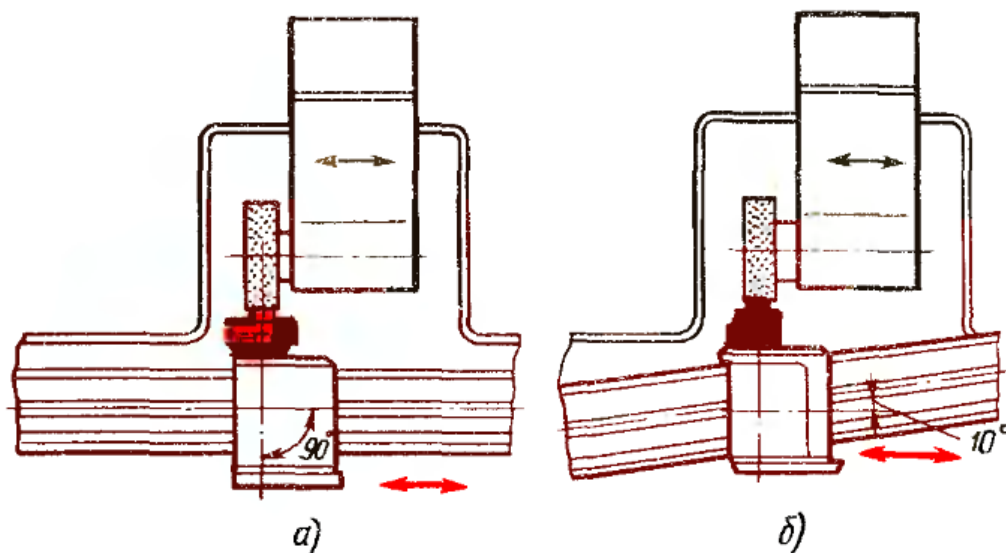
Схема наладки станка для шлифования плоских поверхностей фланцев: а — низко, б — высоко
